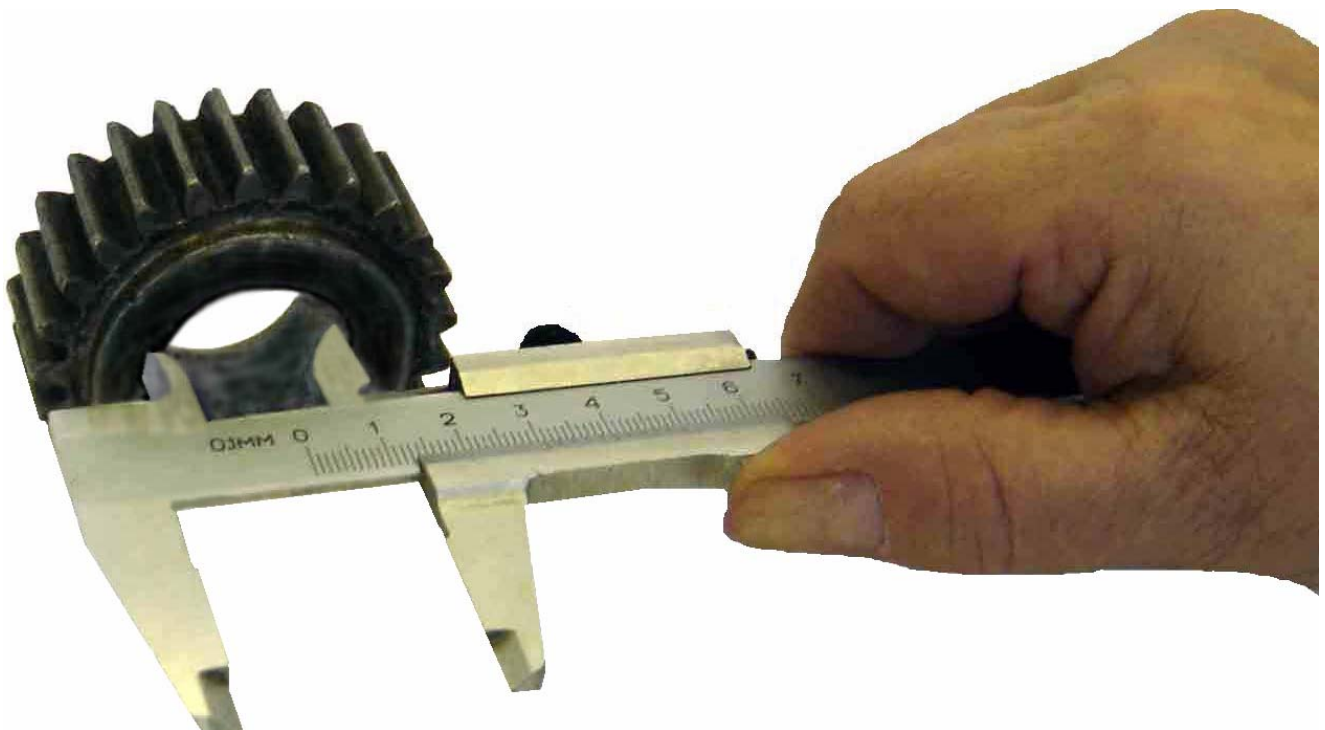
Измерение размера глубины шпоночного паза колеса
